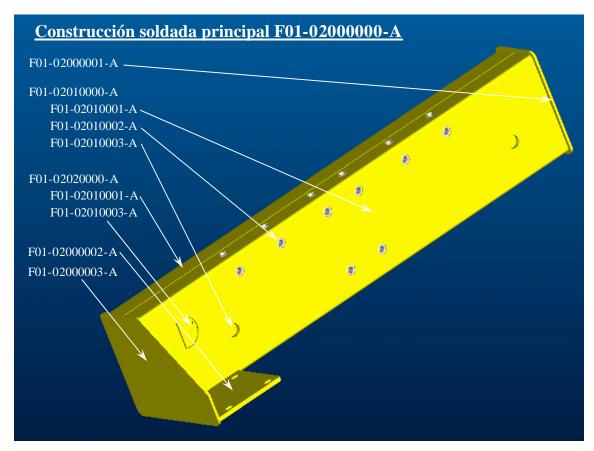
Sub-ensamble F01-02000000-A (Construcción soldada principal).
